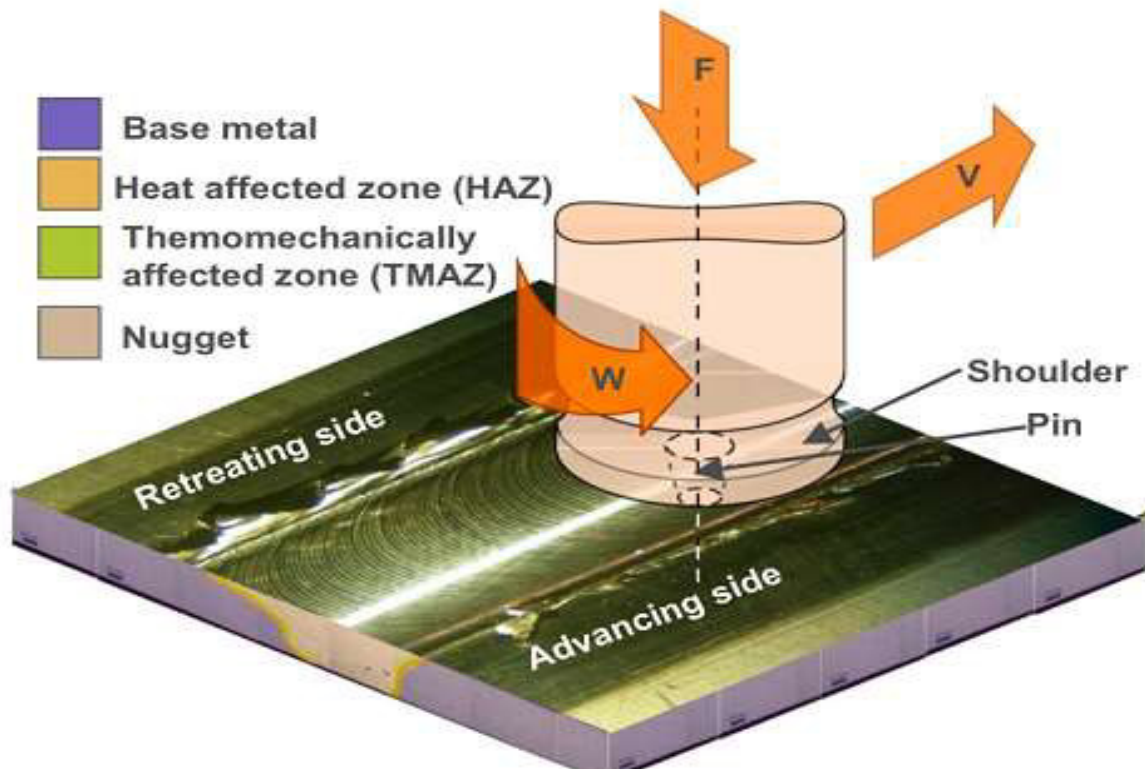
Principe général du procédé de soudage par friction malaxage [22]
